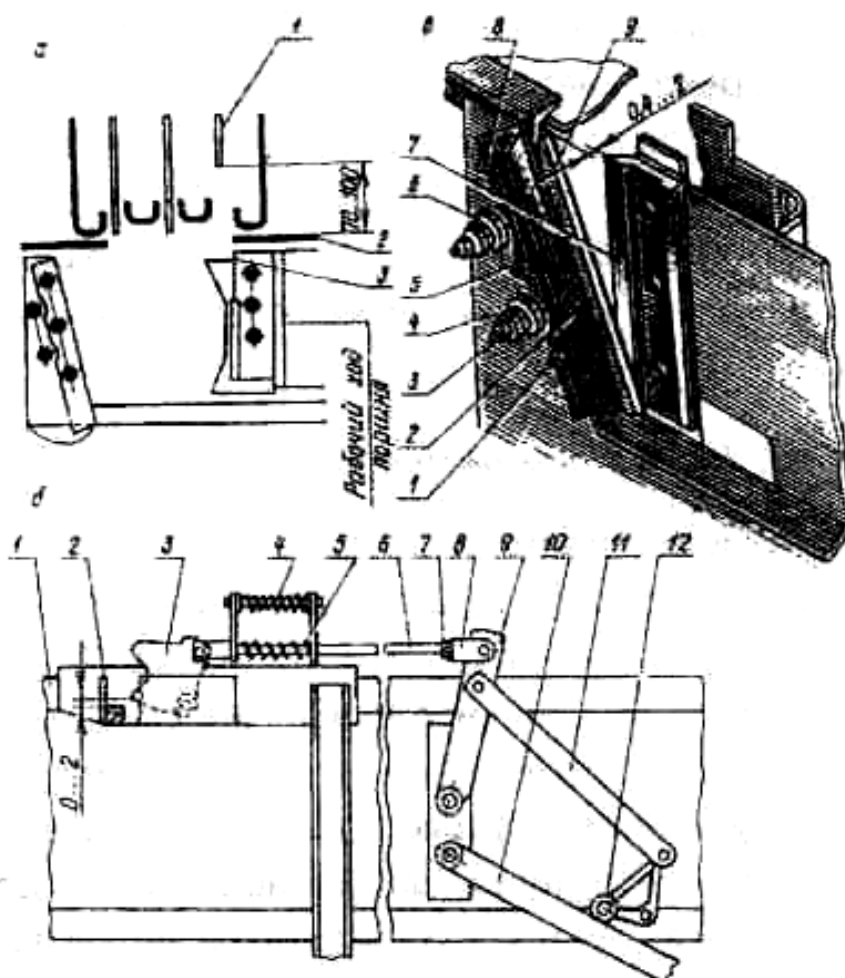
Регулировки пресс-подборщика ПС-1,6
